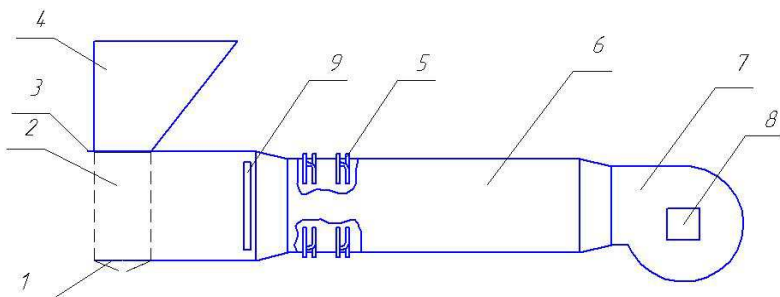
Схема макета установки для тепловой обработки зерна:
